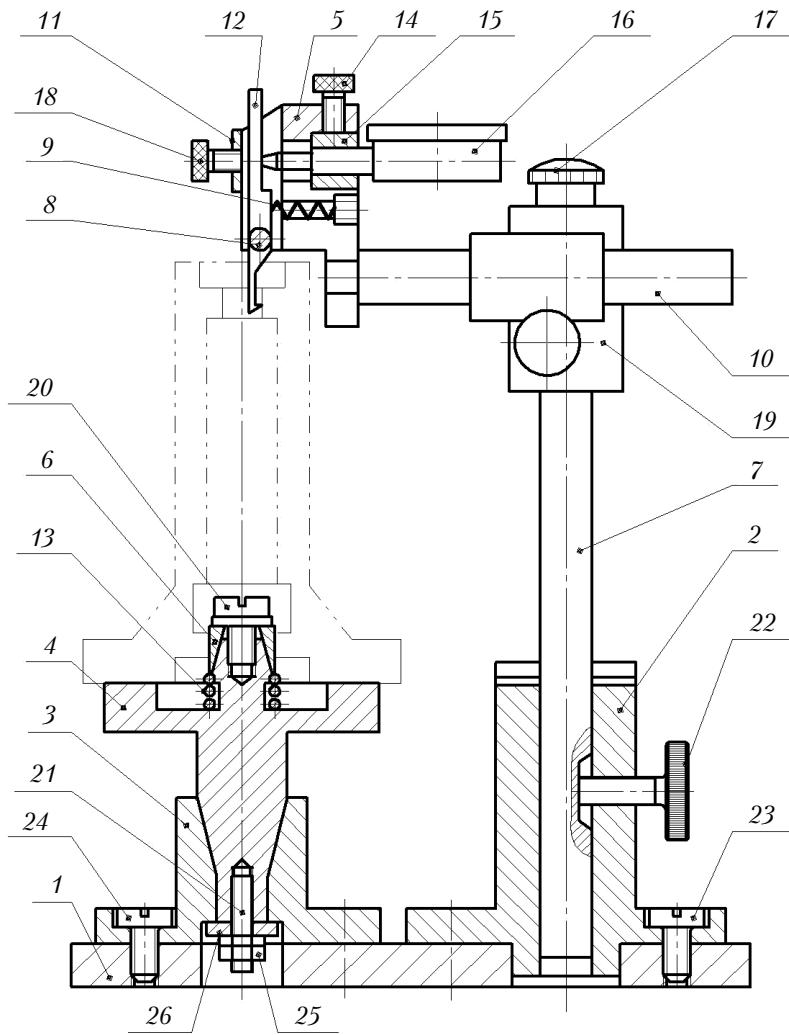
Приспособление для контроля соосности отверстий в корпусной детали:
